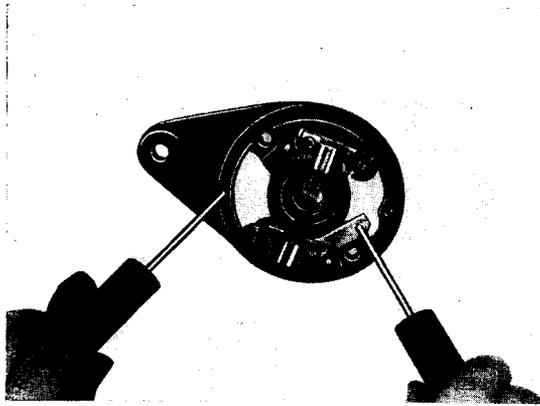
Isolierten Bürstenhalter auf Masseschluß prüfen
